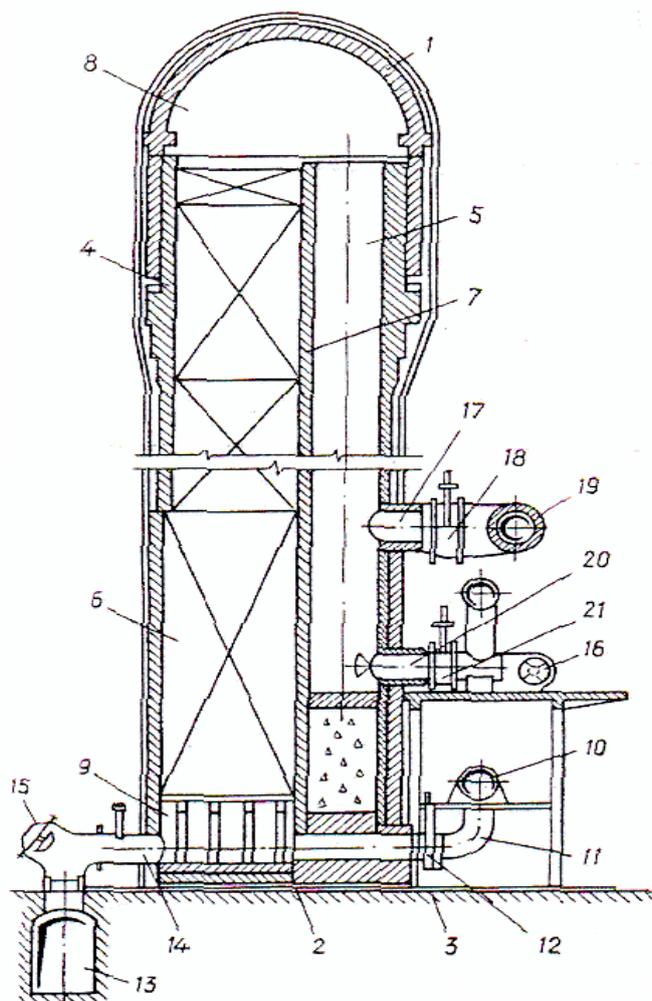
Общий вид воздухонагревателя с внутренней камерой горения:
